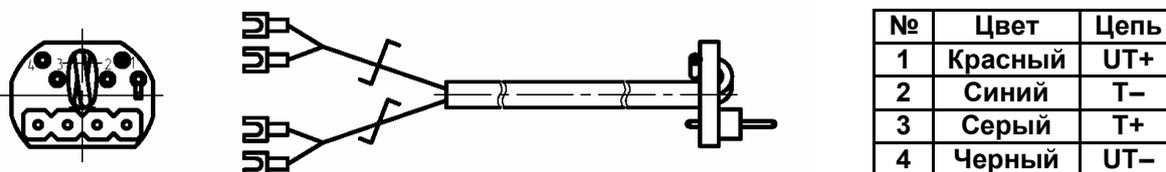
Соединитель канала T1 (006.104.000)
